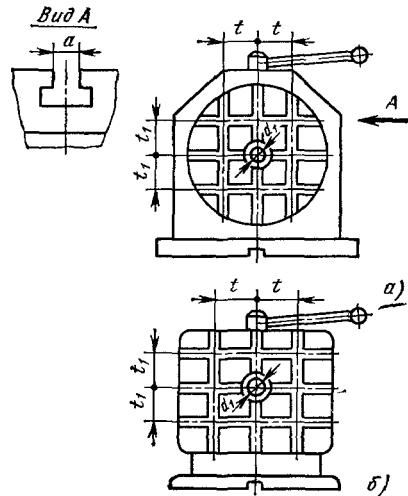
Унифицированные конструктивные элементы УБП для установки заготовок:
